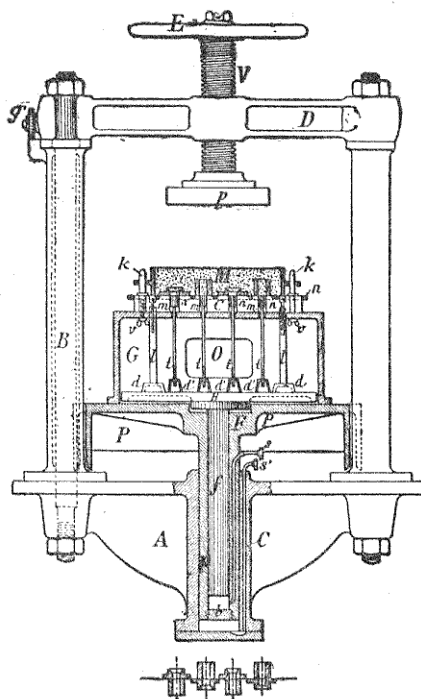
Machine à mouler Bonvillain et Ronceray, à serrages hydraulique et mécanique combinés.
